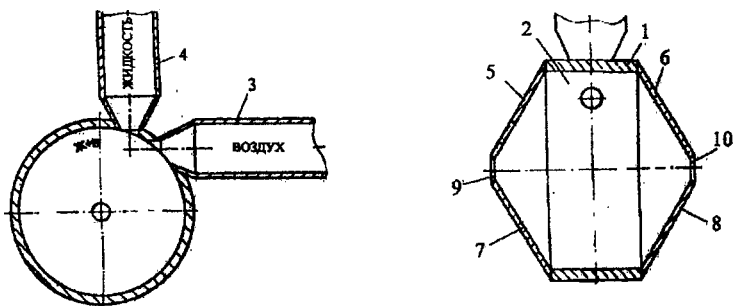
Центробежный двусторонний пневматический распылитель жидкости
